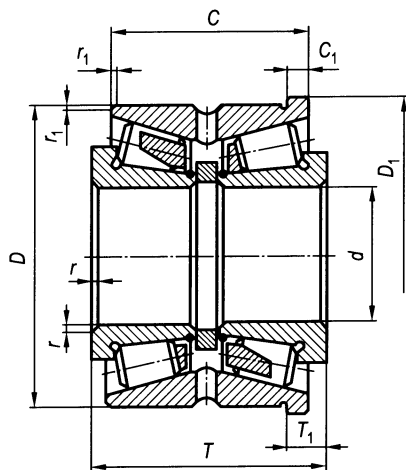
Подшипник роликовый радиально-упорный конический двухрядный с бортом на наружном кольце
